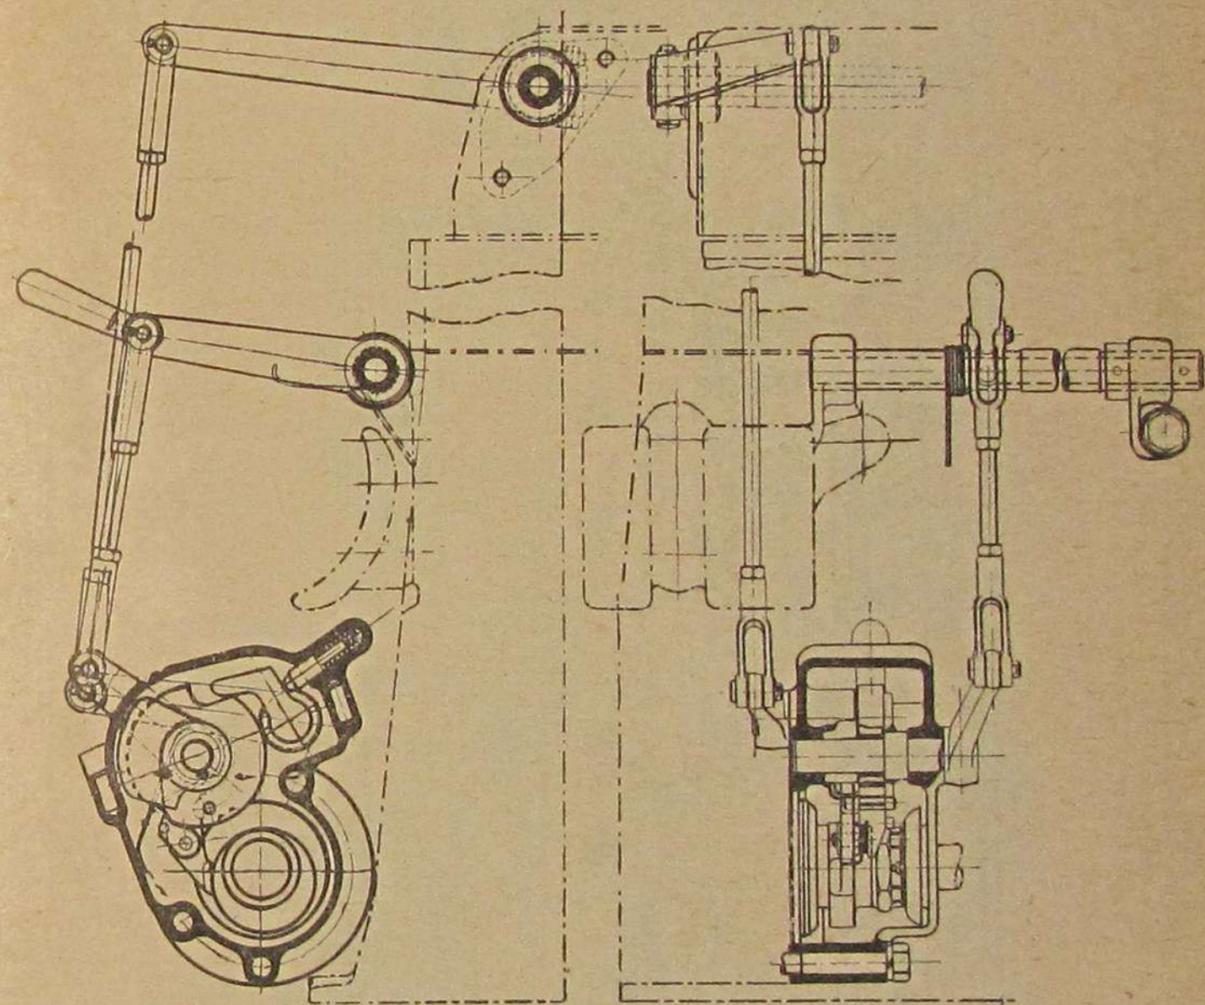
Декомпрессионный механизм двигателя НАТИ М-12.
